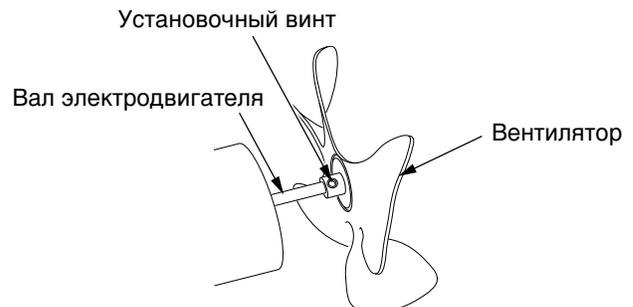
Расположение вентилятора, вала электродвигателя и установочного винта
